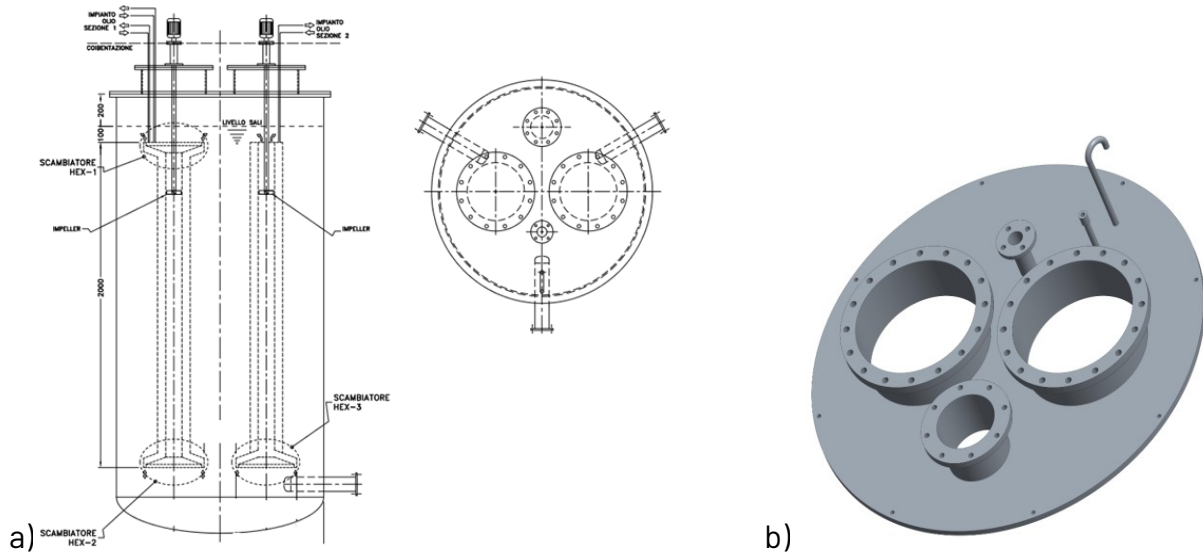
a) Vista in sezione e vista dall'alto del serbatoio, b) vista 3D del coperchio
